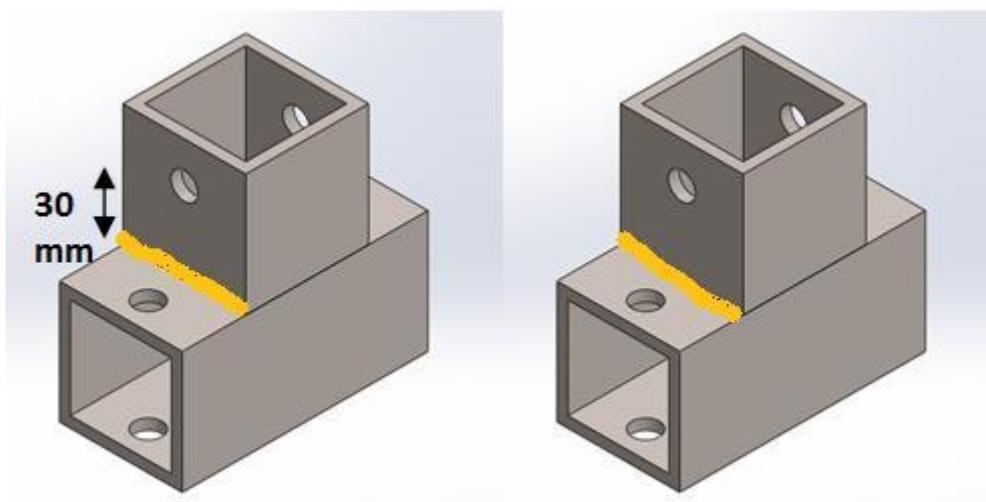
Indicação, a traço amarelo, dos locais onde se realiza soldadura na peça.
